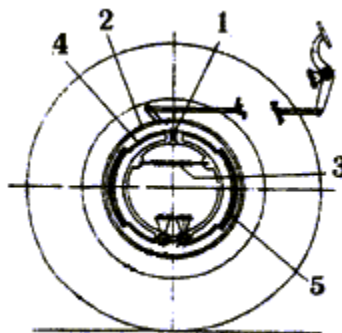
Пристрій гальмової системи із пневматичним механізмом:
